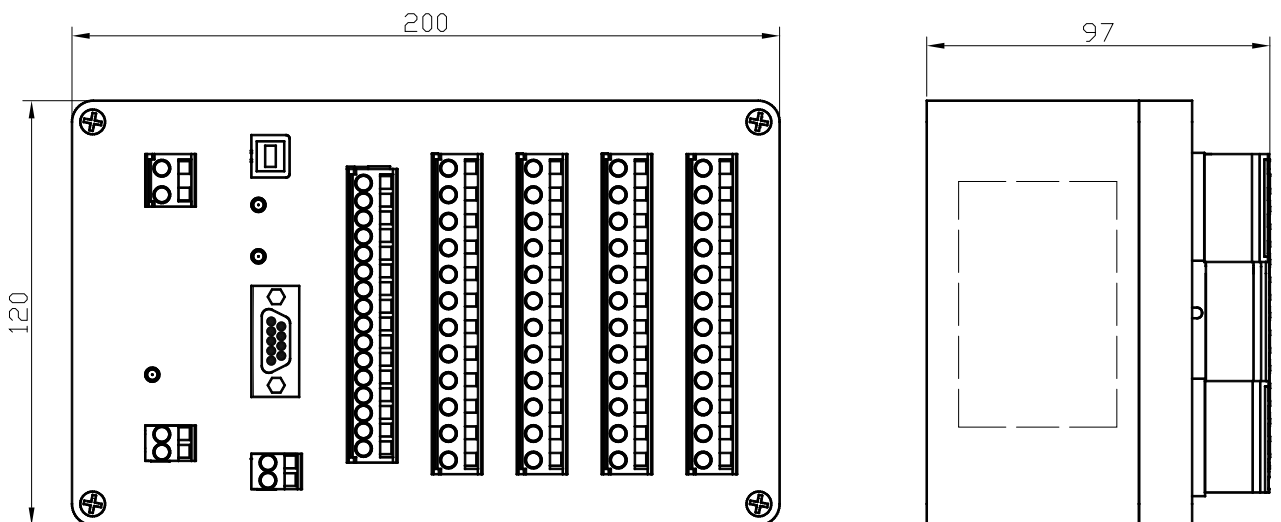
Габаритные размеры контроллера с четырьмя МСД
